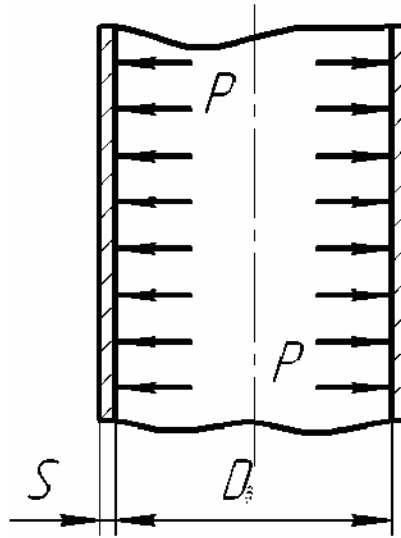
Розрахункова схема циліндричної обичайки
